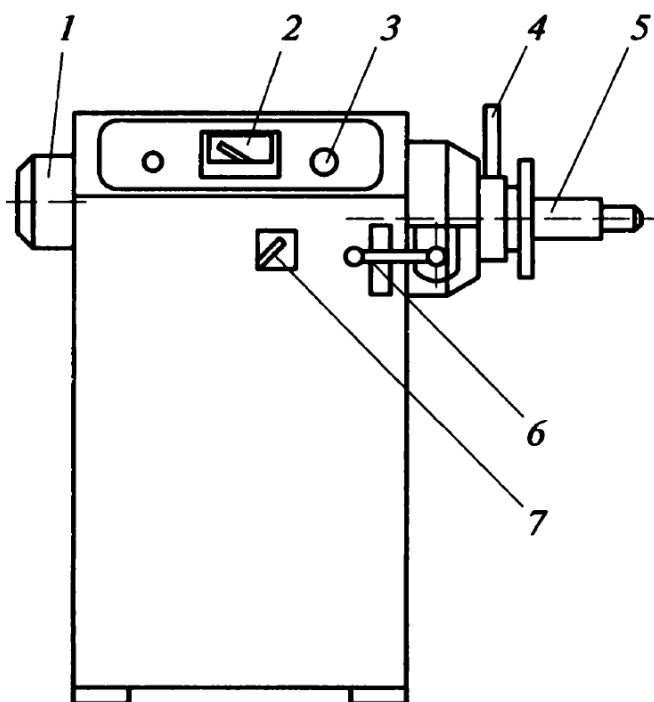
Стенд AMR-2 для балансировки колес: 1 — градуированный диск места дисбаланса; 2 — измеритель массы балансирующего грузика; 3 — регулятор размерности шин; 4 — установочный стержень; 5 — зажимной патрон колеса на валу стенда; 6 — переключатель плоскости балансировки (I и II) колеса; 7 — переключатель привода вращения колеса и тормоза
